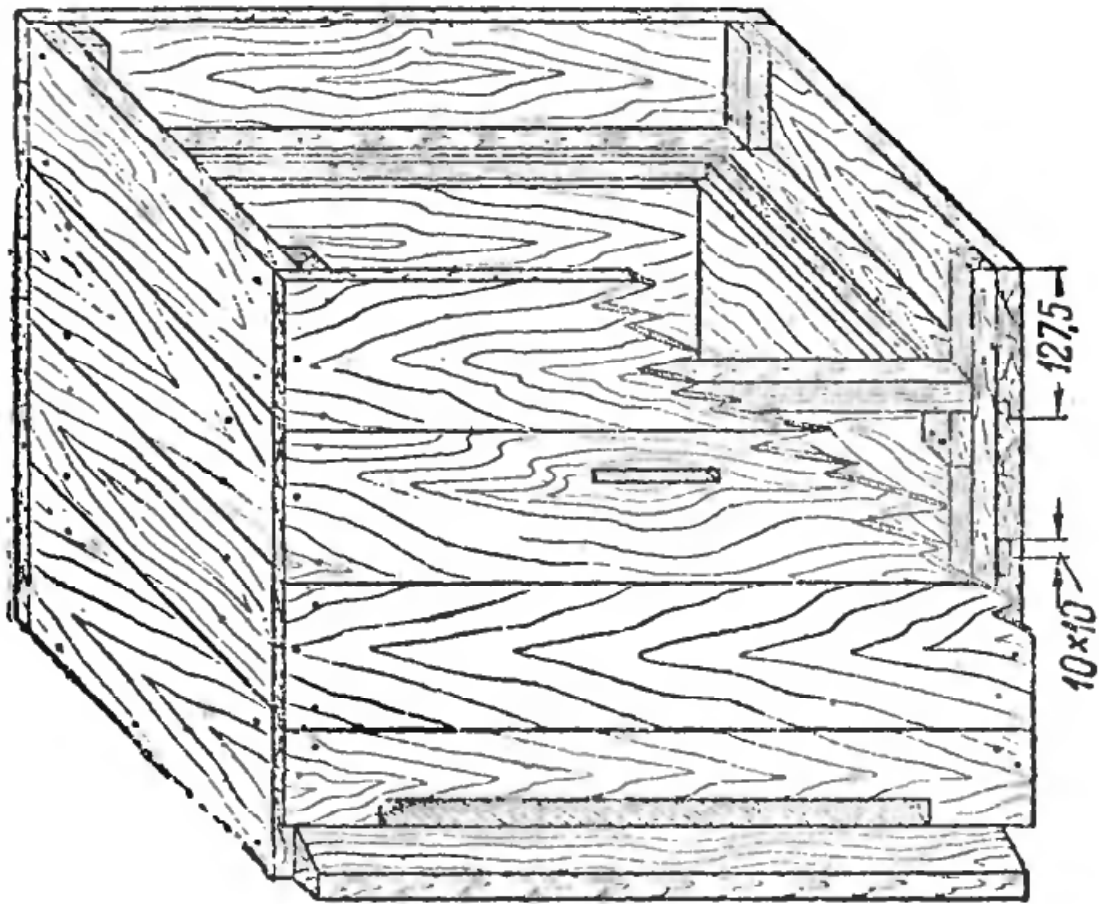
Корпус в готовом виде после установки укупорочных брусков.
